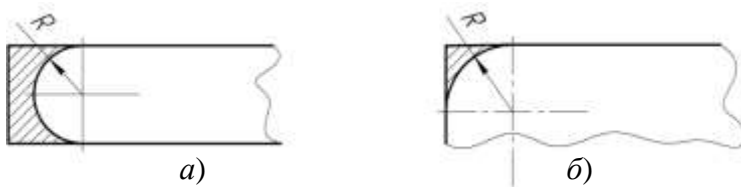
Утворення заокруглень: а) дуга 180° ; б) дуга 90°
